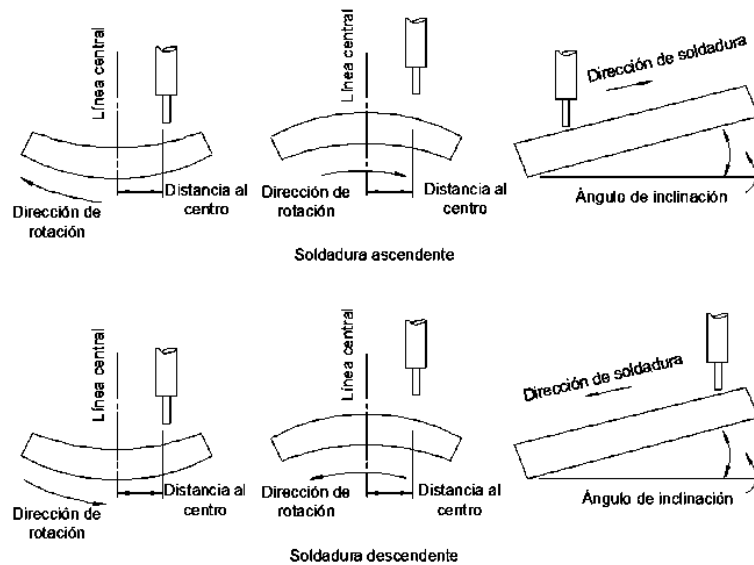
Soldadura ascendente y descendente sobre placas y partes cilíndricas [7]
